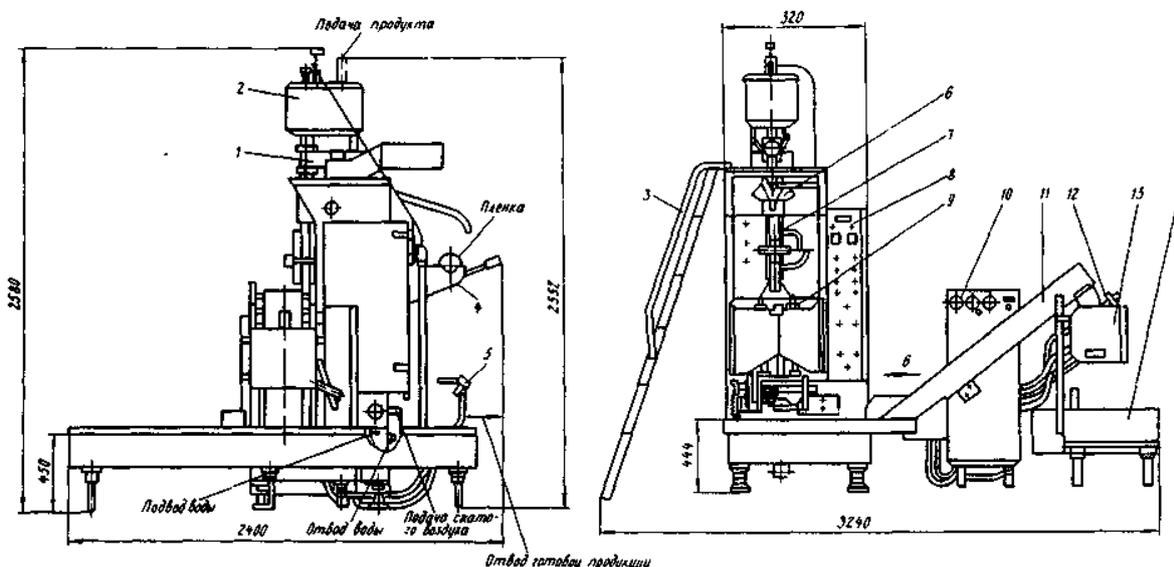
Общий вид автомата марки М6-ОРЗ-Е для розлива молока в полиэтиленовые пакеты: 1 - поршневой дозатор; 2 - бункер; 3 - лестница; 4 - рулонодержатель; 5 - отвод готовой продукции; 6 - рукавообразователь; 7 - механизм сварки продольного шва; 8,10 - шкаф электрооборудования; 9 - механизм сварки поперечного шва; 11 - транспортер пакетов; 12 - фотоэлемент счетного устройства; 13 - бункер; 14 - транспортер ящиков
